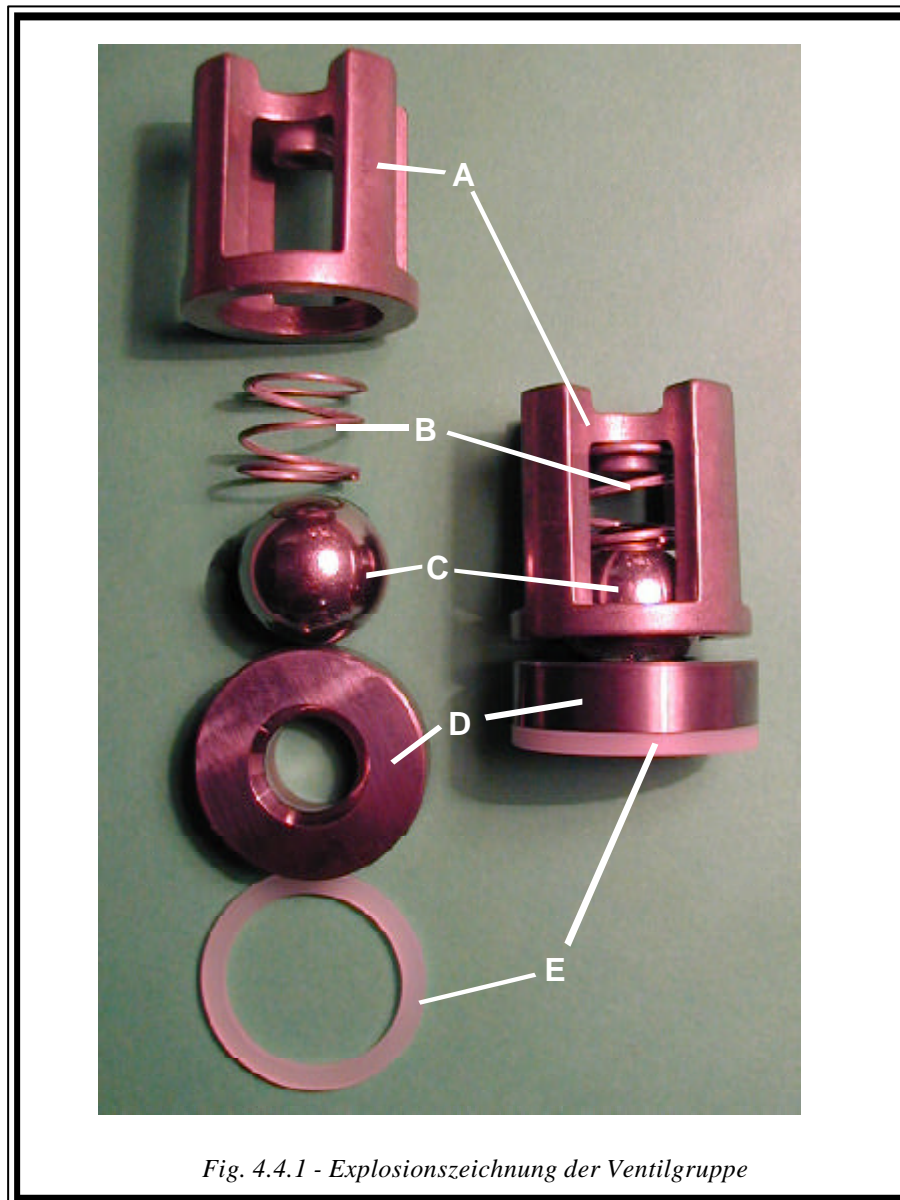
Explosionszeichnung der Ventilgruppe
